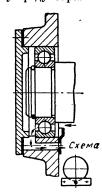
Циркуляционная смазка подшипника (смазка улавливается «порогом»)
